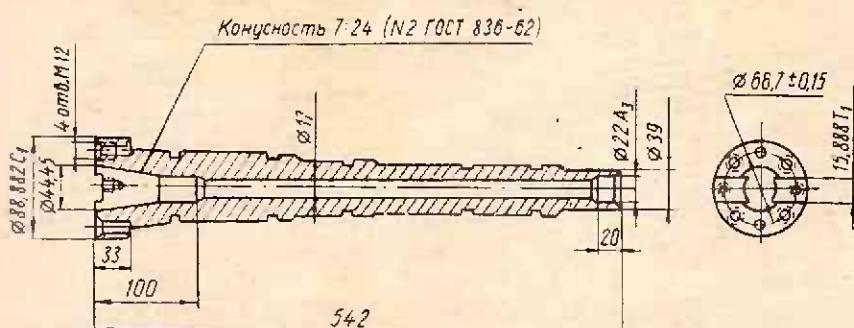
Эскиз шпинделя станков 6Н80Г и 6Н80
